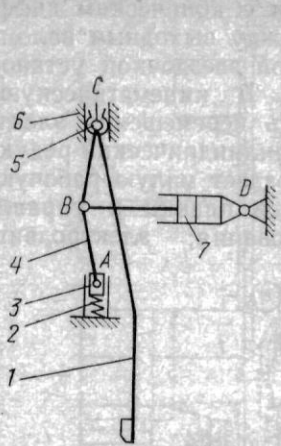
Кинематическая схема механизма прижима кристаллизатора
